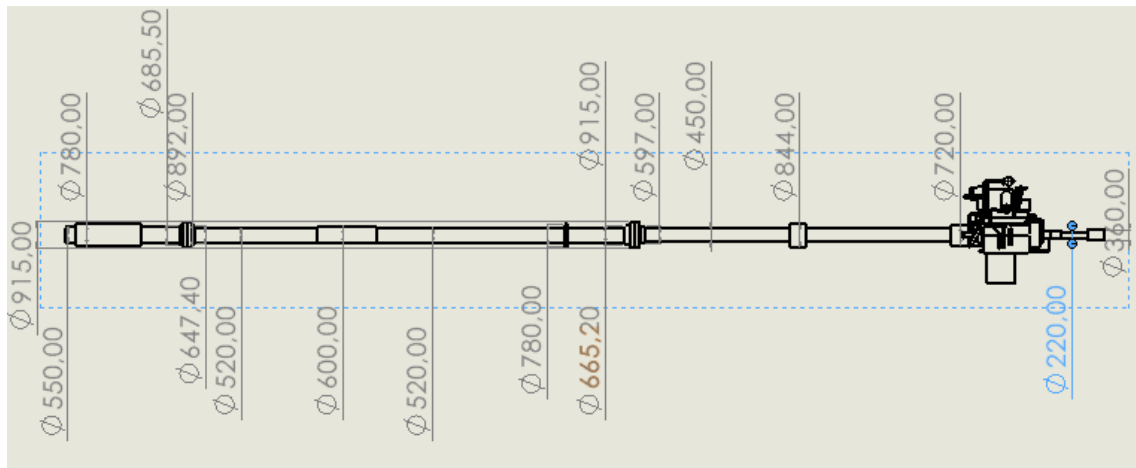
, Plano perfil de la colocación de los apoyos. Fuente: Propia
